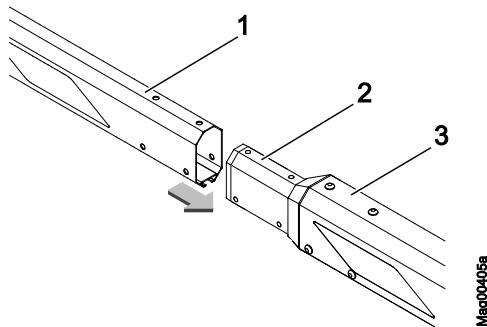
Kleines Baumprofil auf den Verbinder schieben
